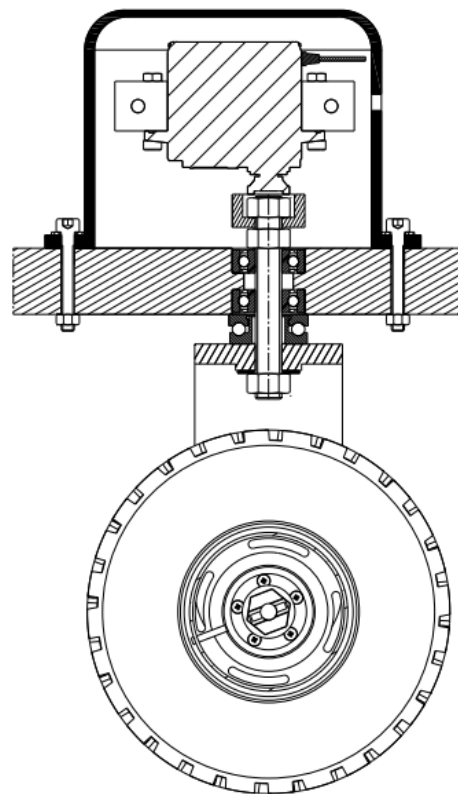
Sección transversal a dispositivo de giro de la rueda.
